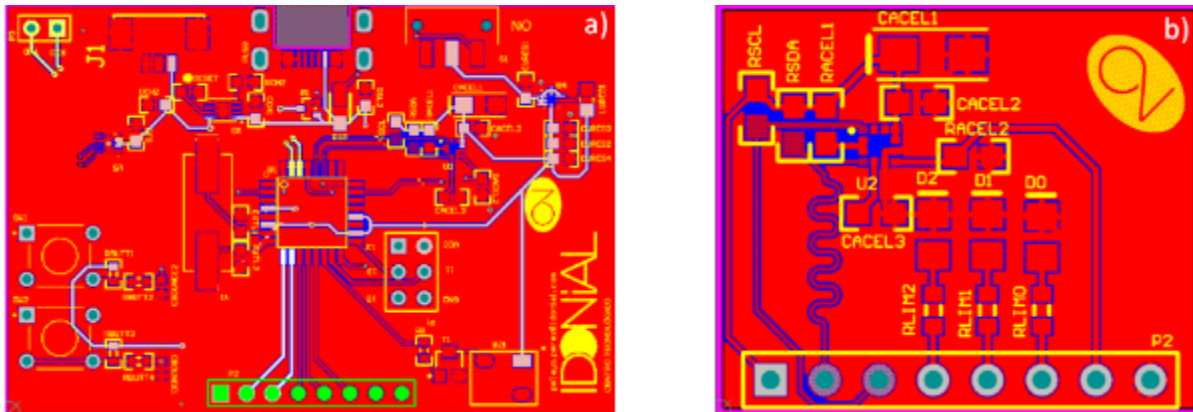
PCBs diseñadas para el dispositivo SMART ARM, a) Placa de control y b) Placa auxiliar.
